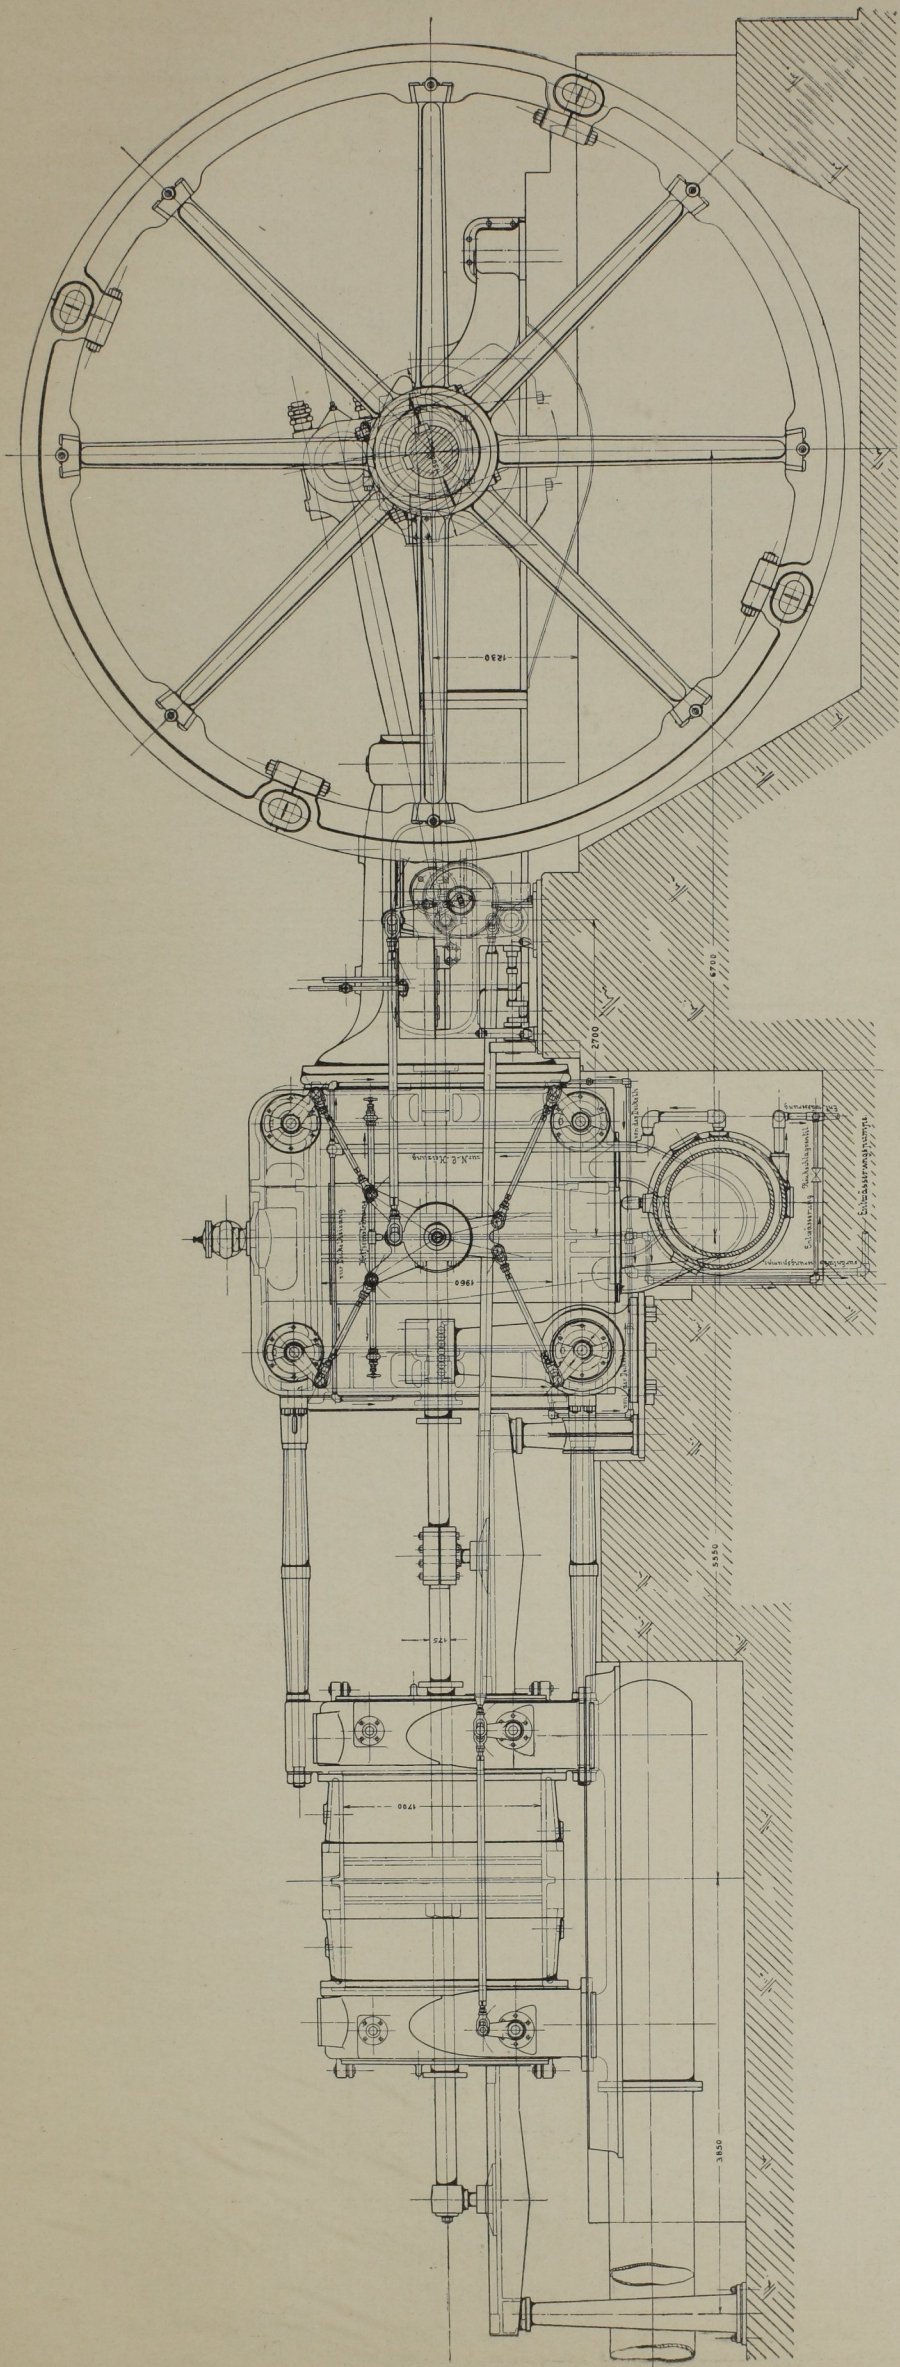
Seitenansicht der Niederdruckseite der Gebläsemaschine. Masst. 1 : 60.
